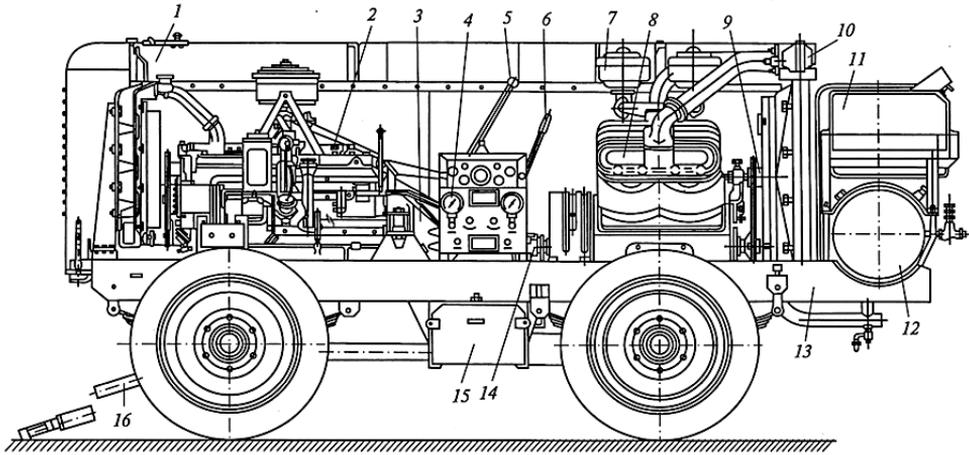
Передвижная мобильная компрессорная установка ПКС-5:
